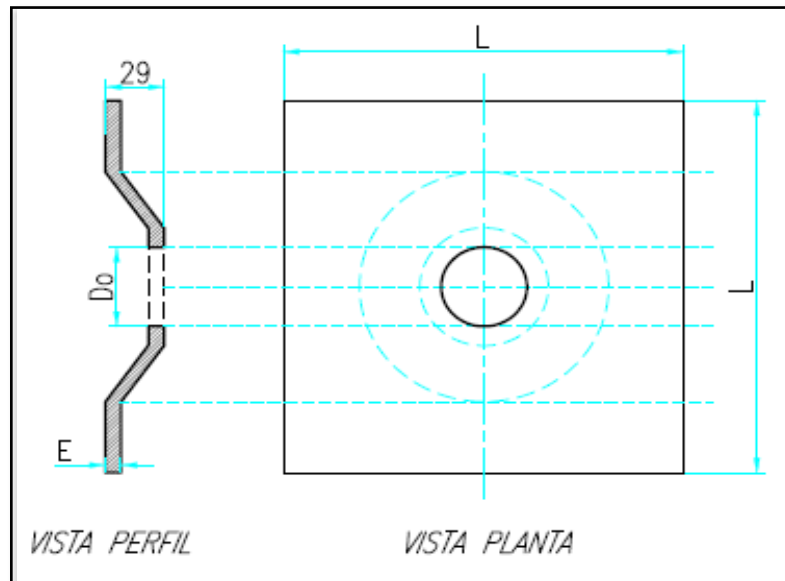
Vista transversal y en planta de la placa de fijación
